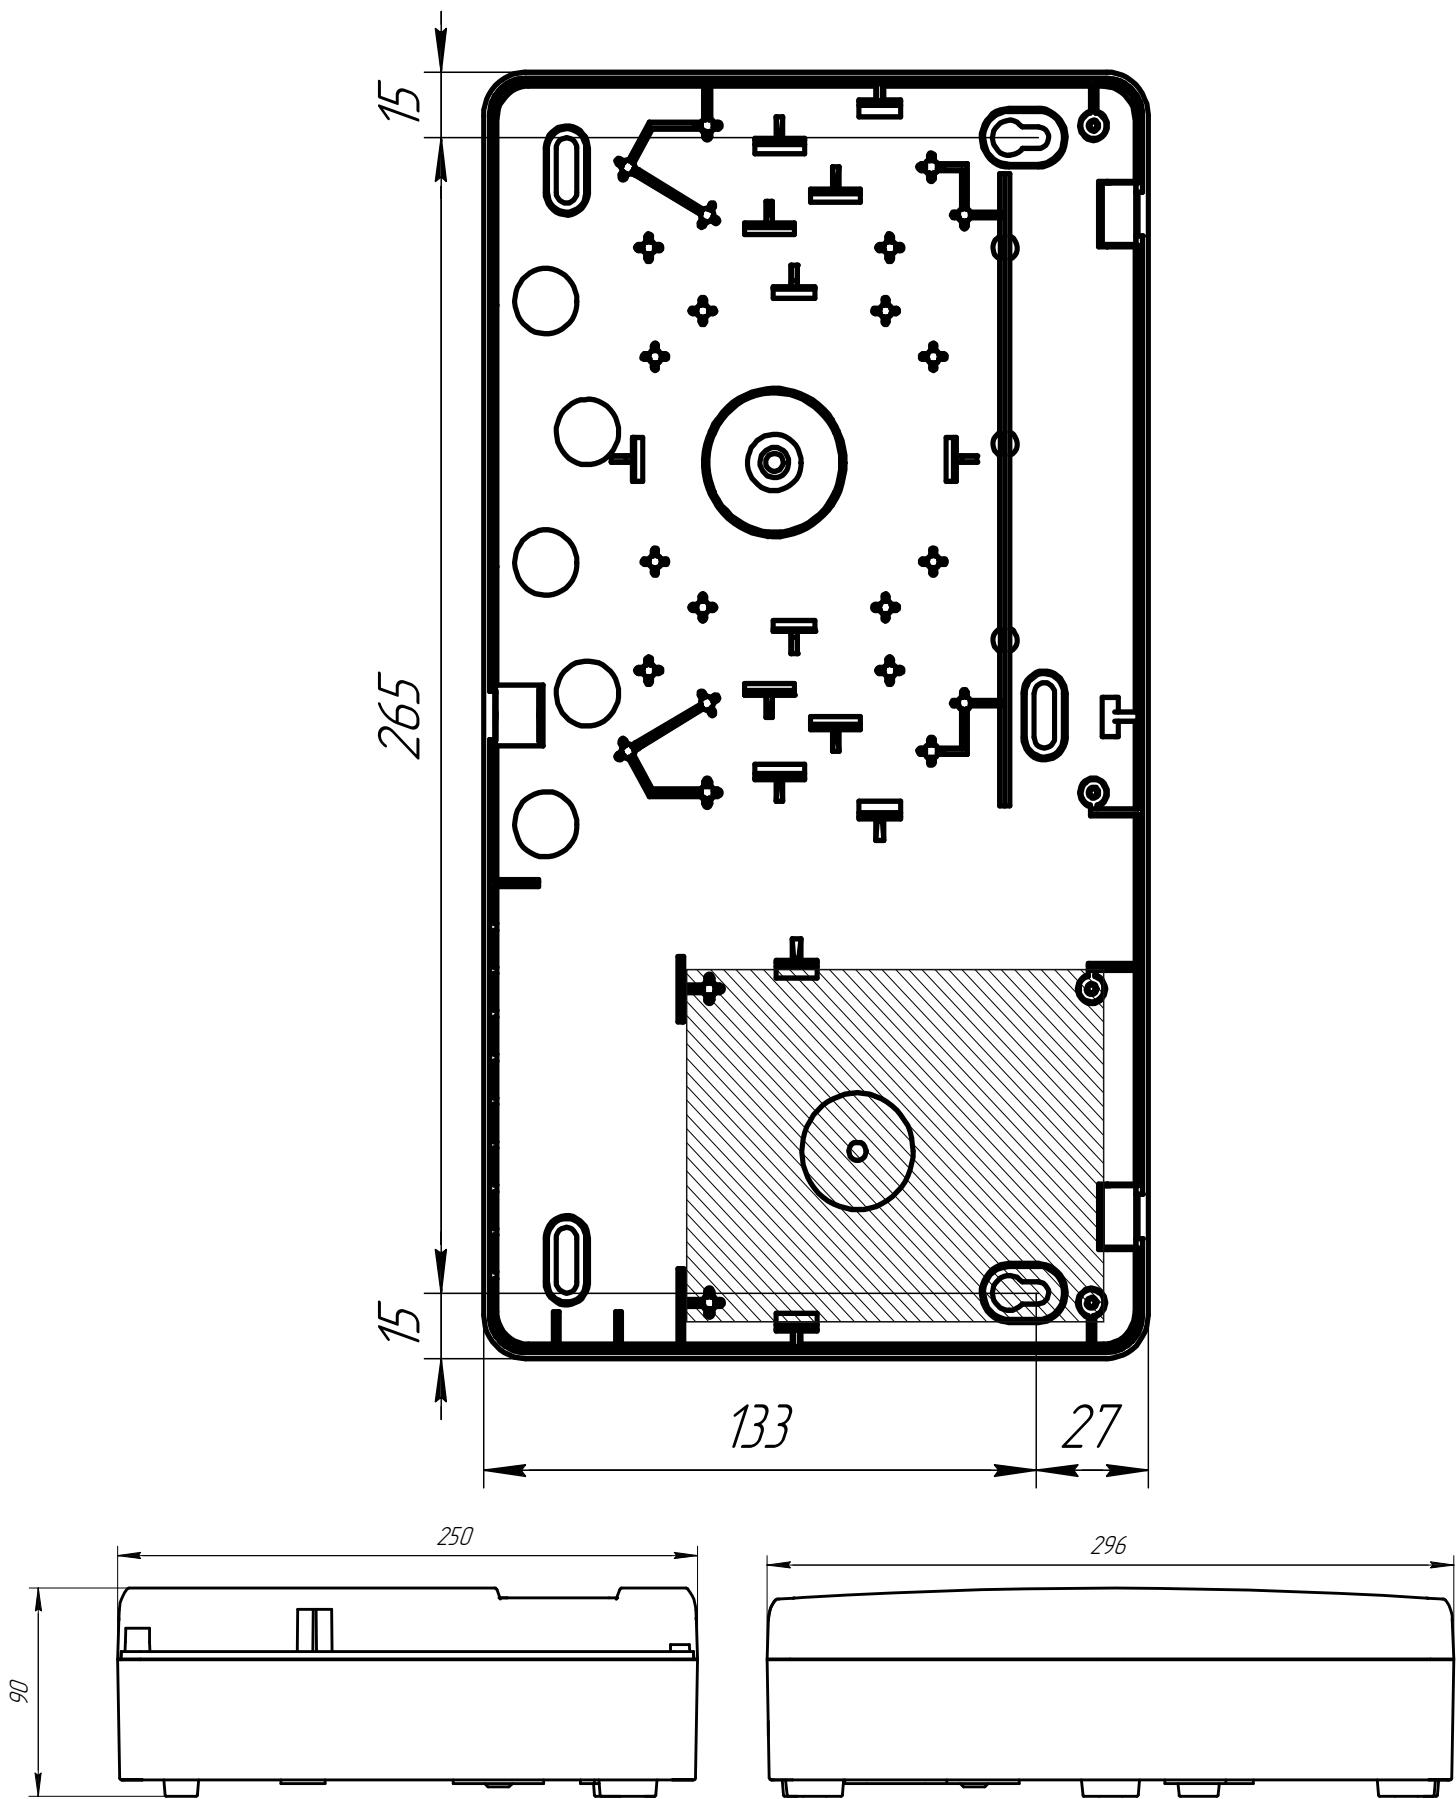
Корпус «Контакт» под АКБ 1.2 Ач
